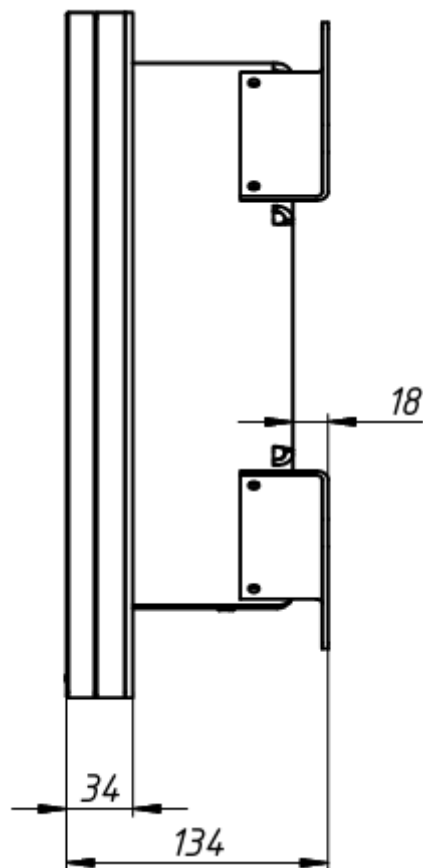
Габаритный чертёж ПИ в исполнении
